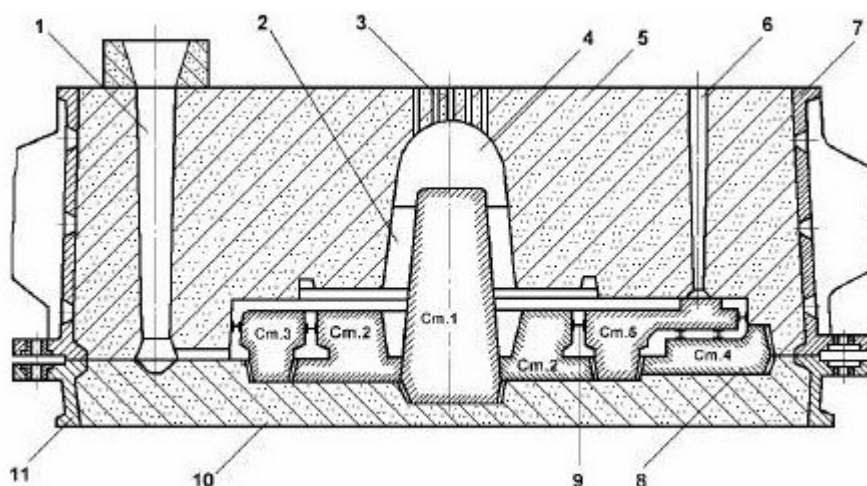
Форма в сборе для отливки “Корпус барабана”
